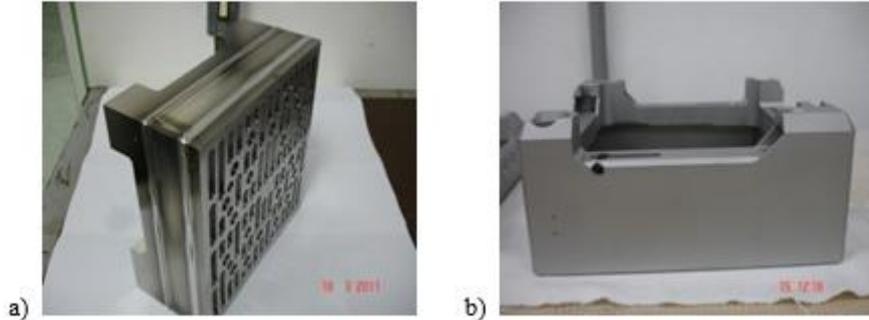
a) Projeto da solda da caixa e a cantoneira e b) Solda EBW executada para o projeto.
